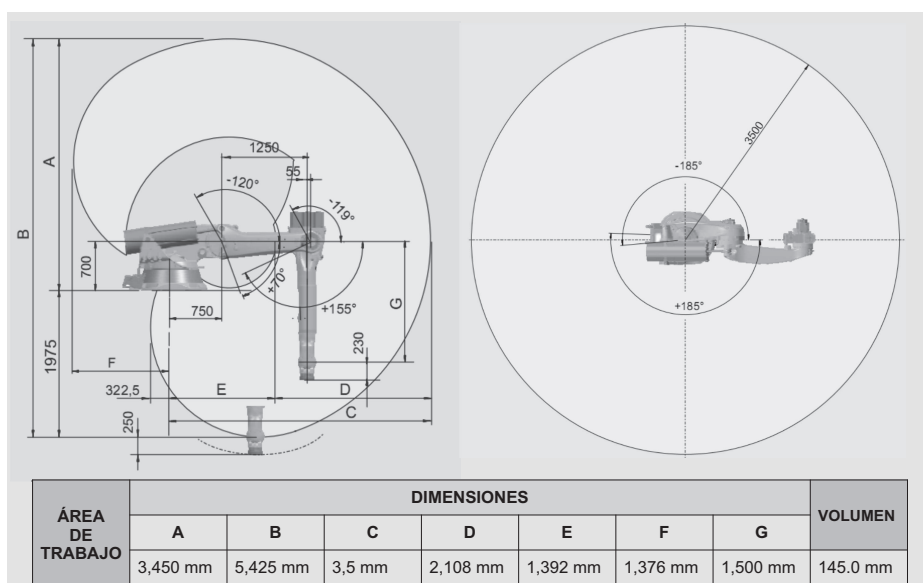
Dimensiones del robot KUKA KR120-2P®.
